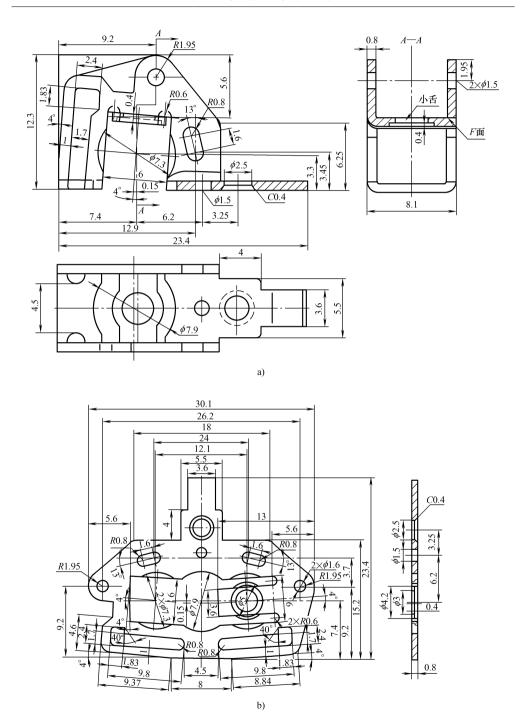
凹形槽级进模 a) 零件图 b) 展开图
